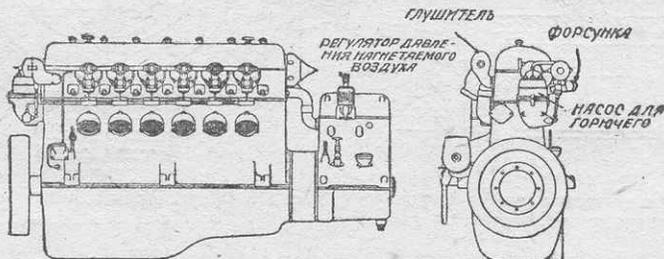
Компрессорный шестицилиндровый дизель «Майбах» с размерами 6 цилиндров 140—180. Мощность 150 л. с. при 1200 оборотах вала в мин. Вес—8 кг на 1 л. с.
